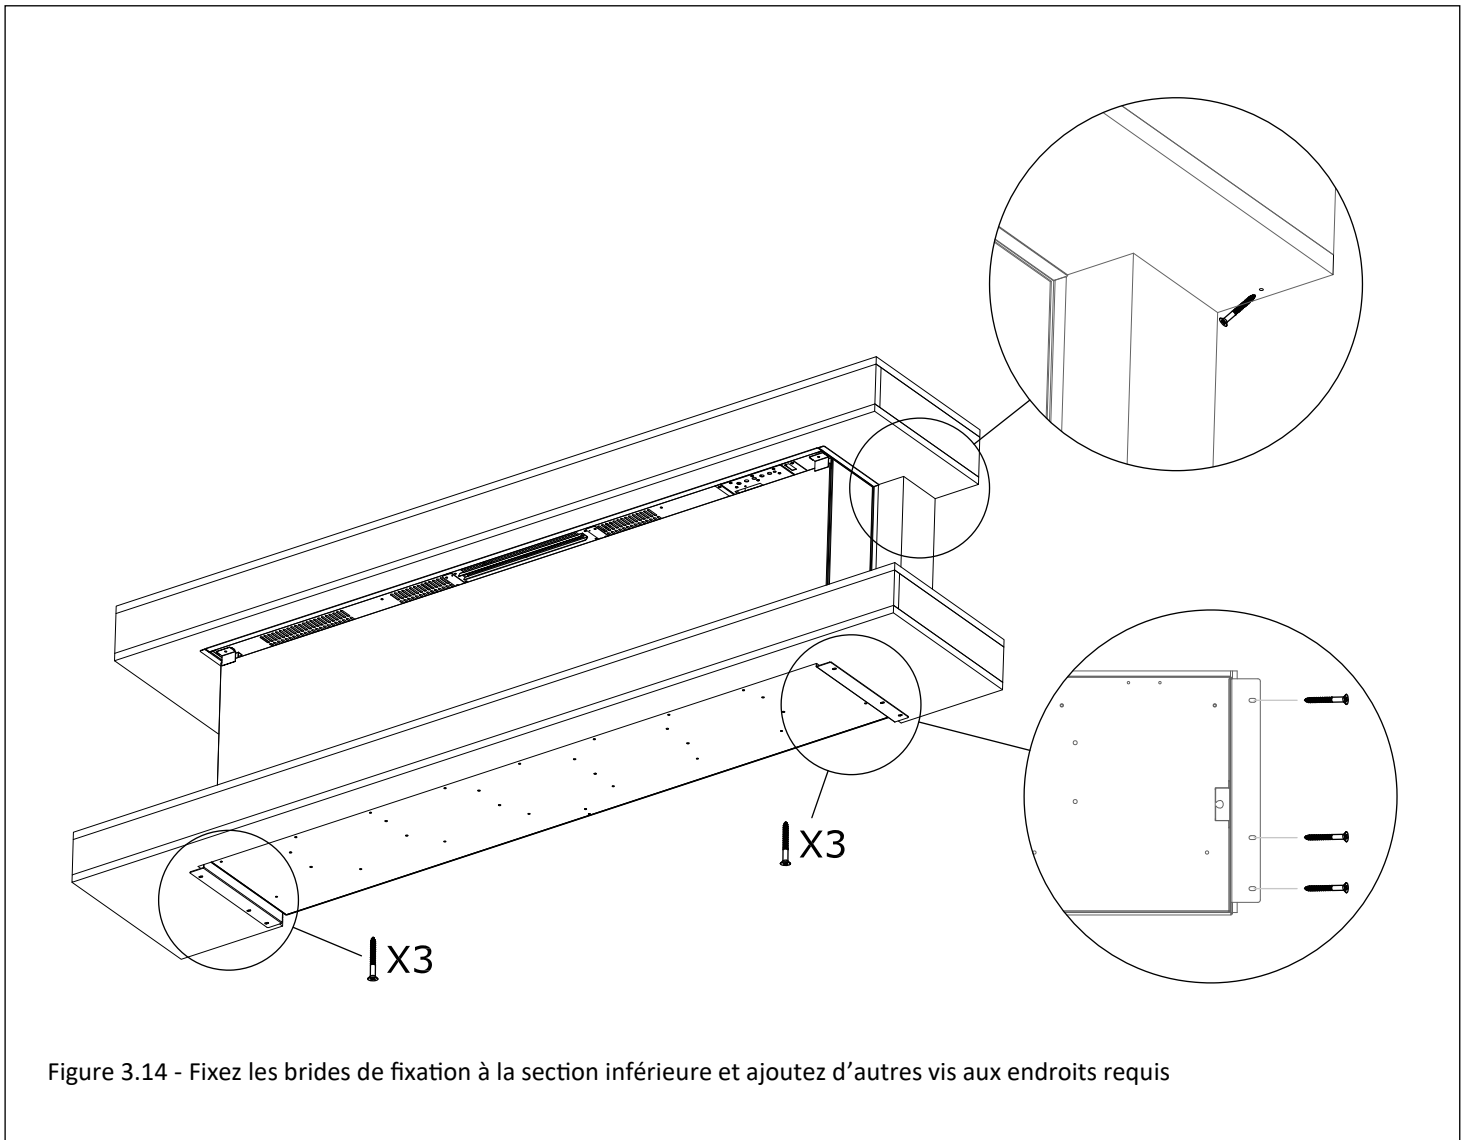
Fixez les brides de fixation à la section inférieure et ajoutez d'autres vis aux endroits requis
